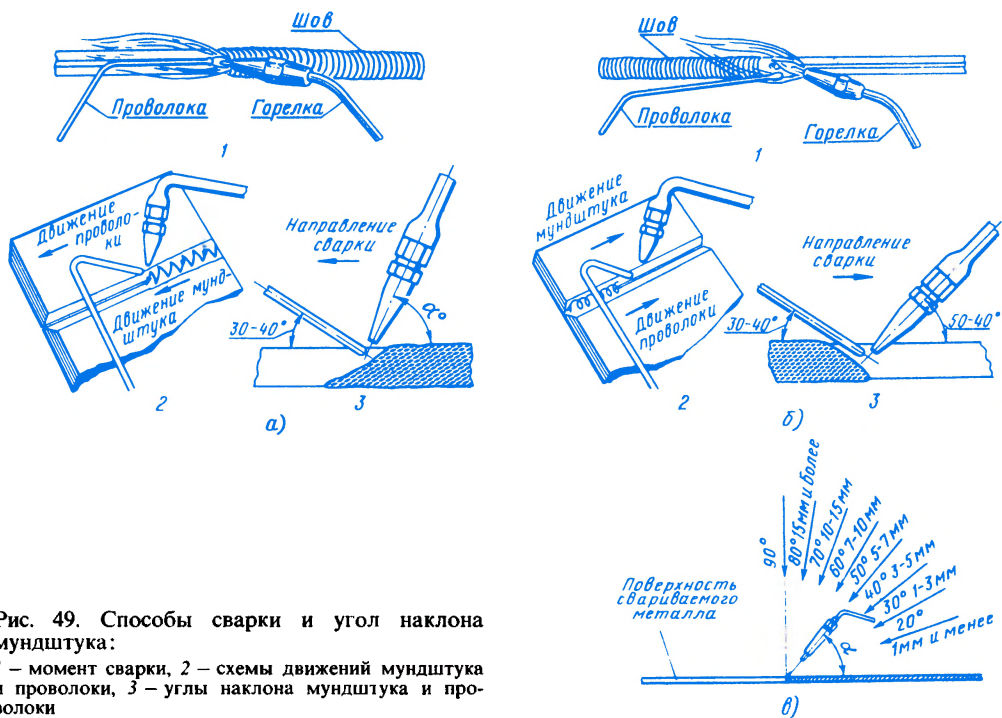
Способы сварки и угол наклона мундштука:
